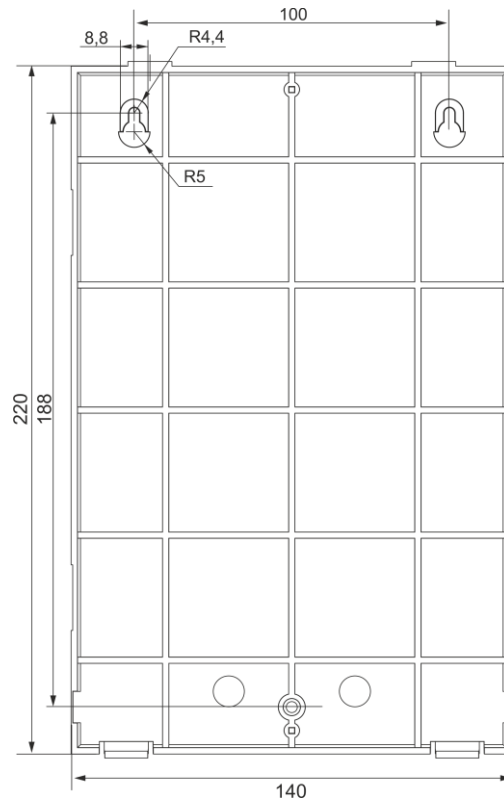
Установочные и габаритные размеры основания корпуса ВПИУ-М, ВПИУ-Б
